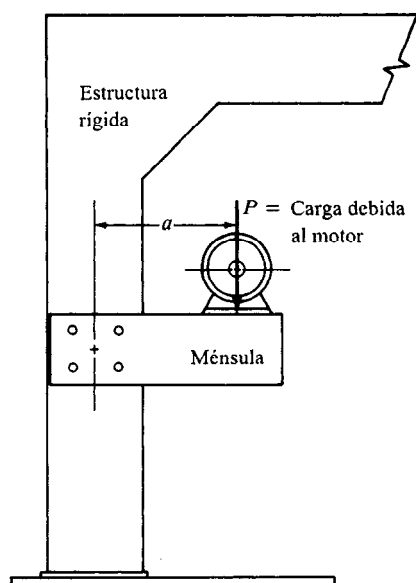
Ensamble soldado que se somete a una carga excéntrica
